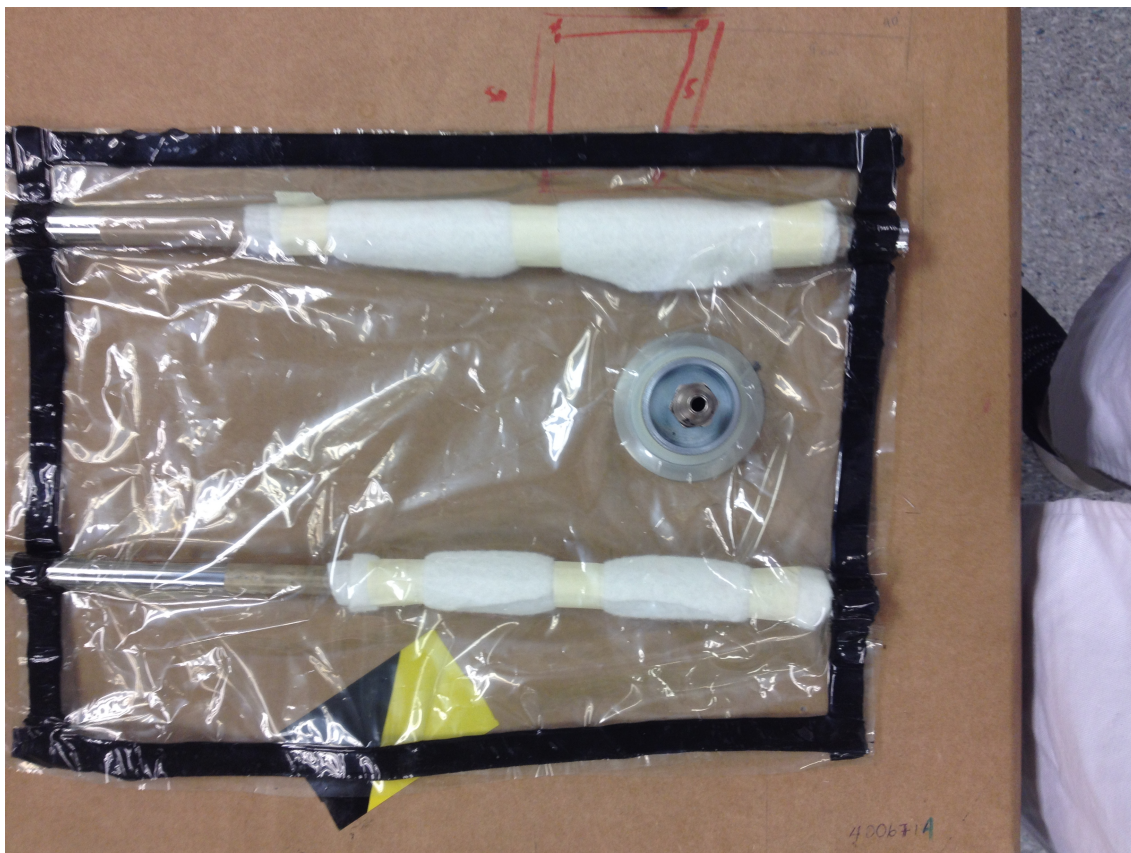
Experimento 1. Montaje (Fuente: Propia)
